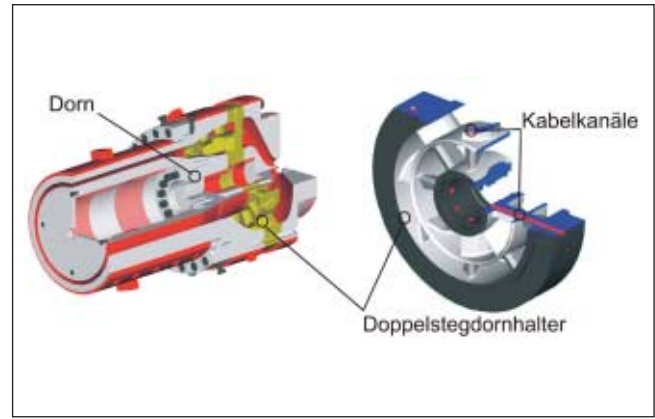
Skizze eines Dornhalterwerkzeugs mit Doppelstegdornhalter (Quelle: Battenfeld Extrusionstechnik)
